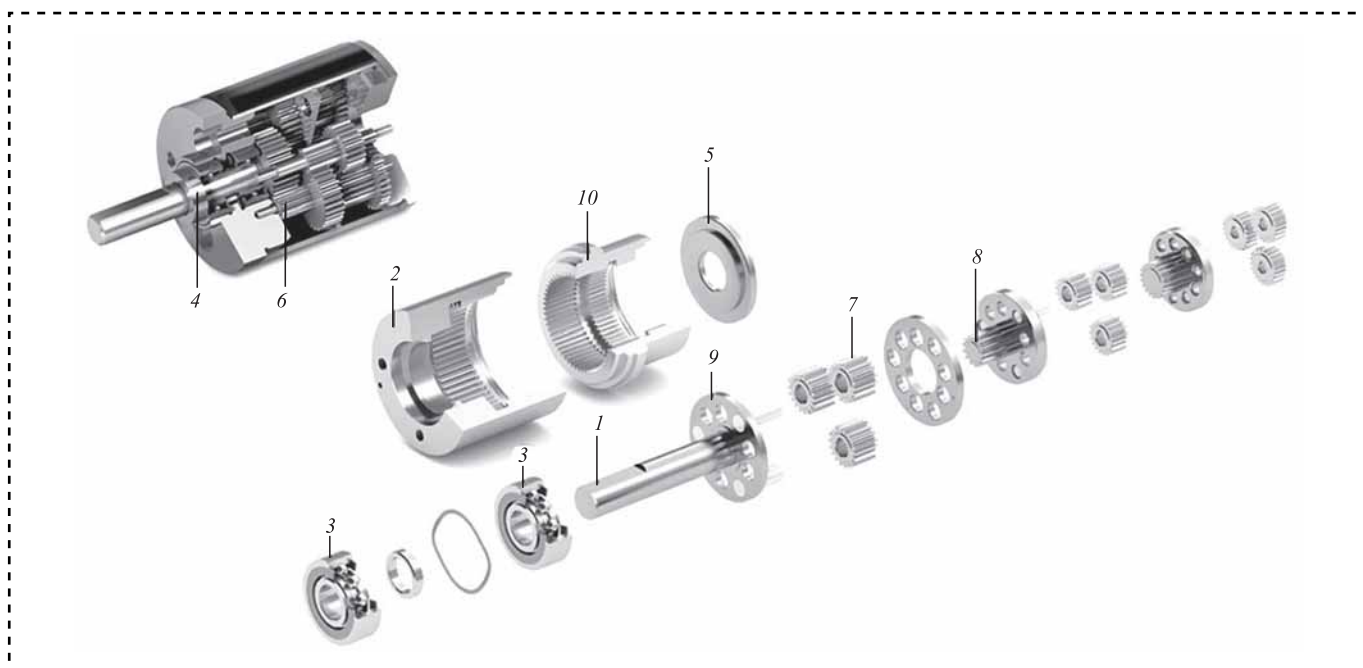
Двигатель постоянного тока MAXON MOTOR:
